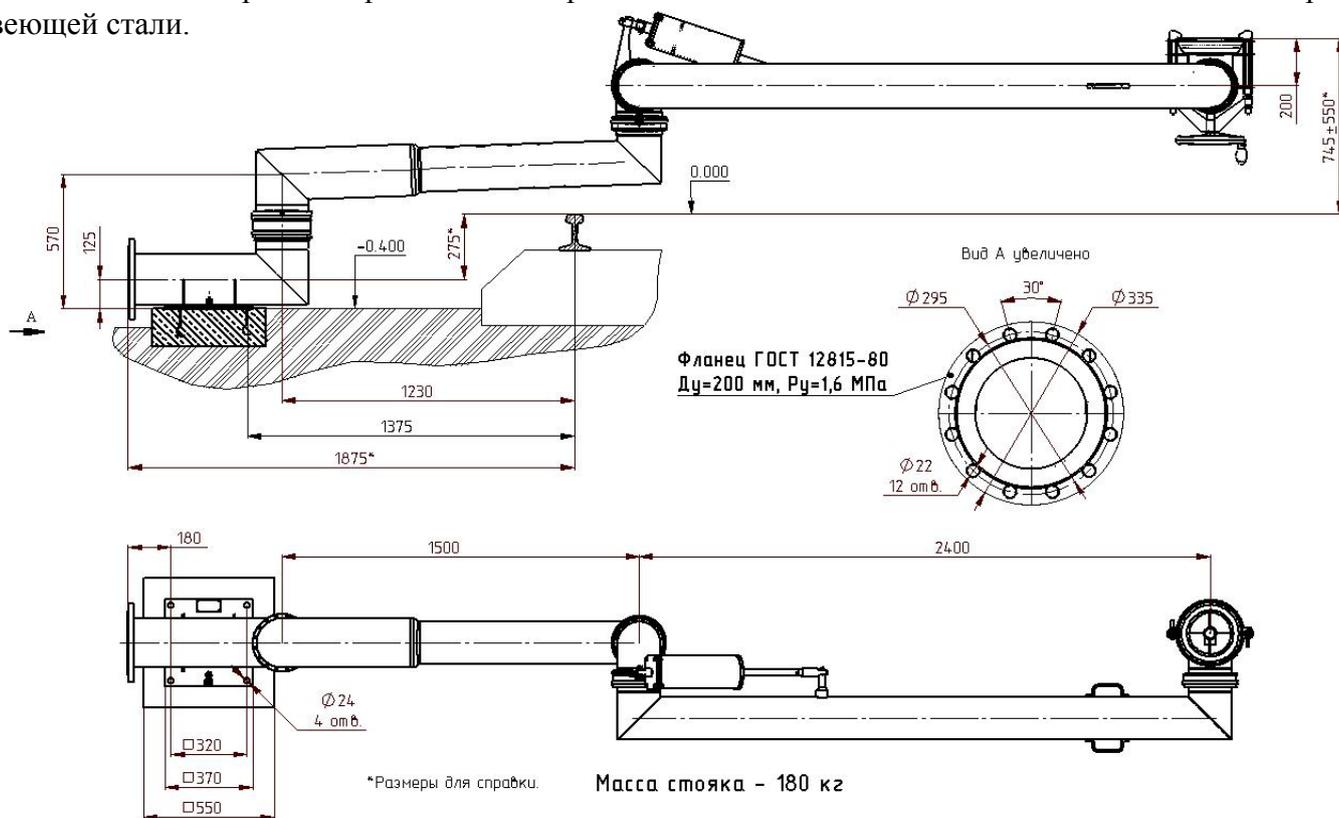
Установочные и габаритные размеры стояка ОСН-СНС-175-НЖ-6.
